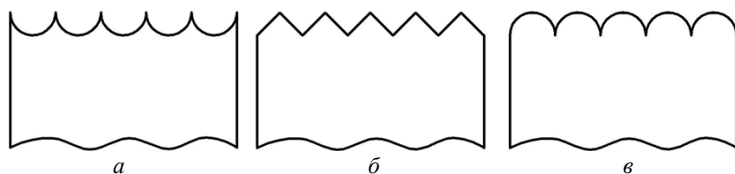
Микропрофили шероховатой поверхности детали:
